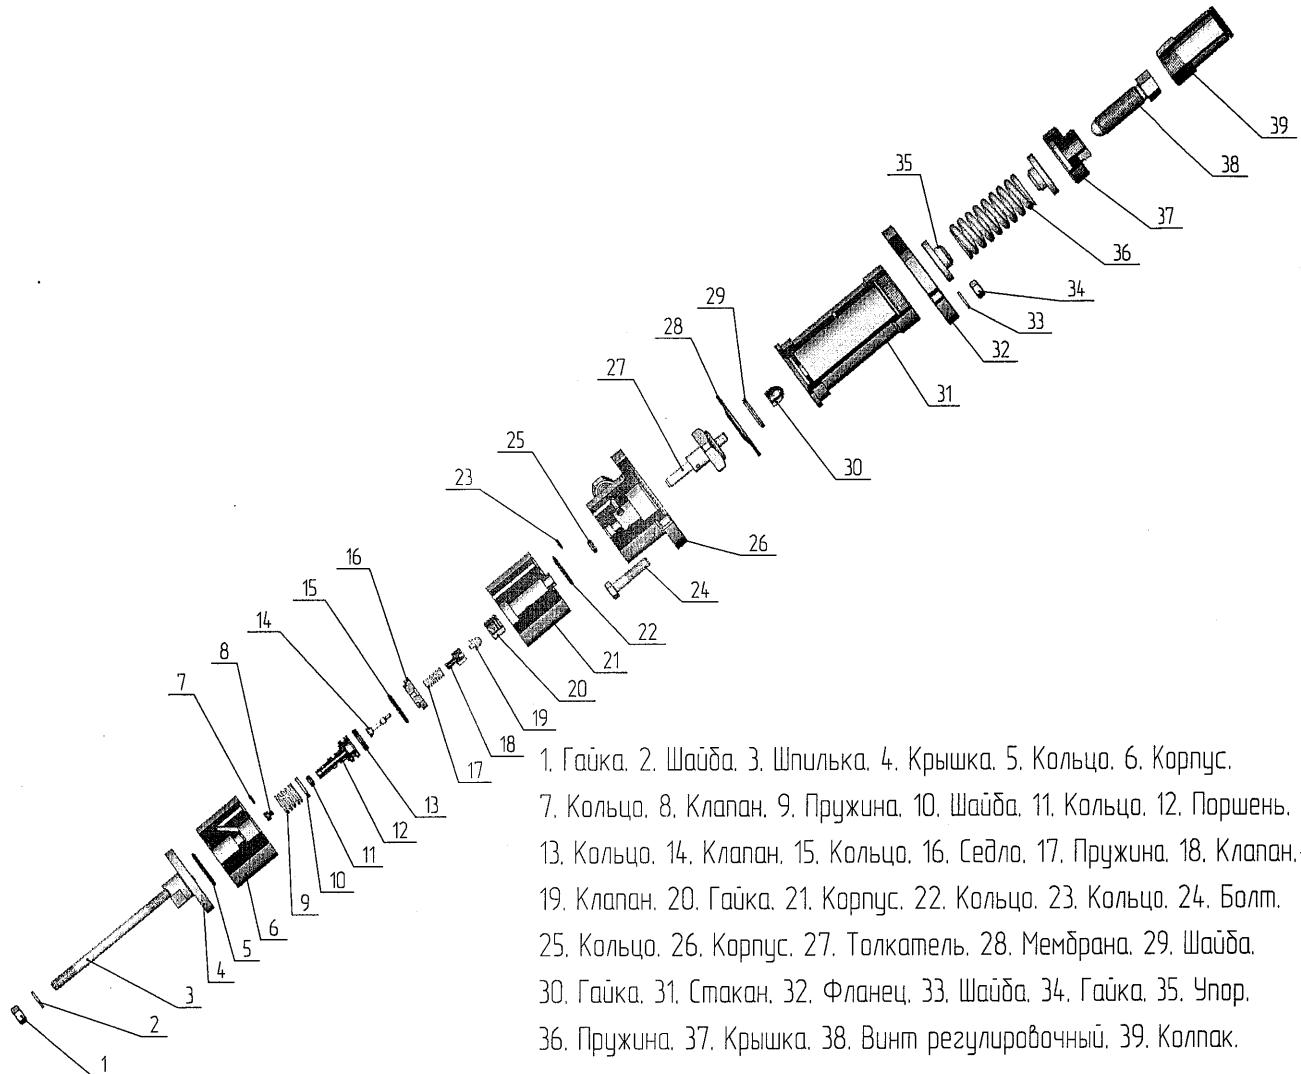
Схема разборки-сборки устройства задающего ЗУ-3.
